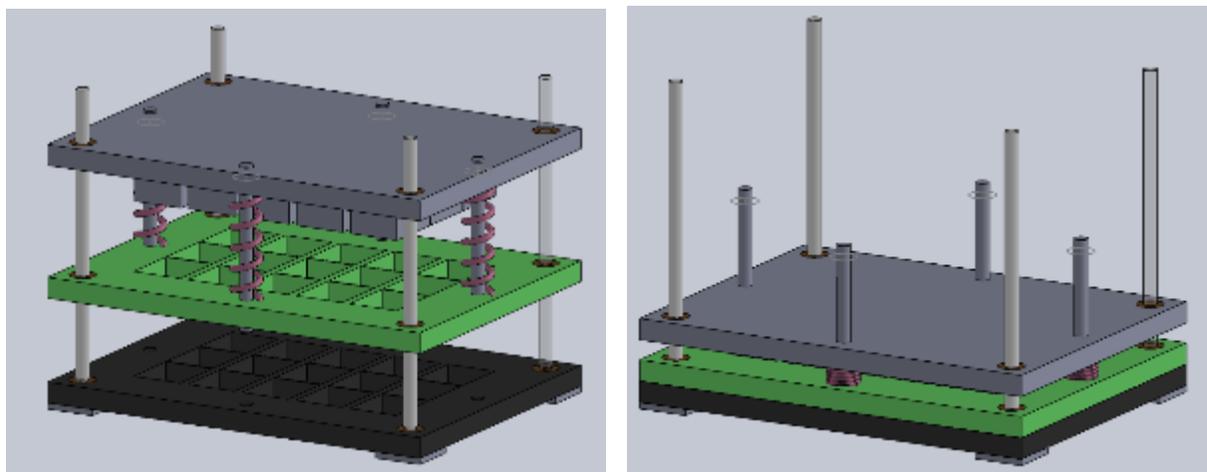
(izq.) Posición inicial; (der.) posición de corte.
